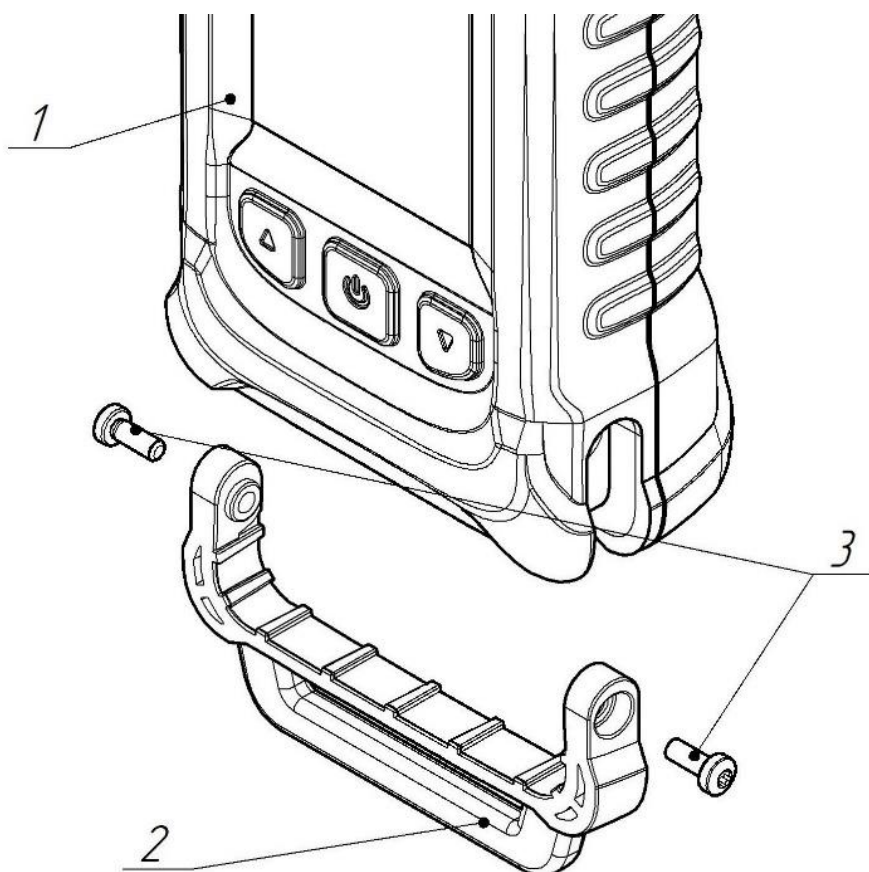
Внешний вид процедуры замены держателя ремня
